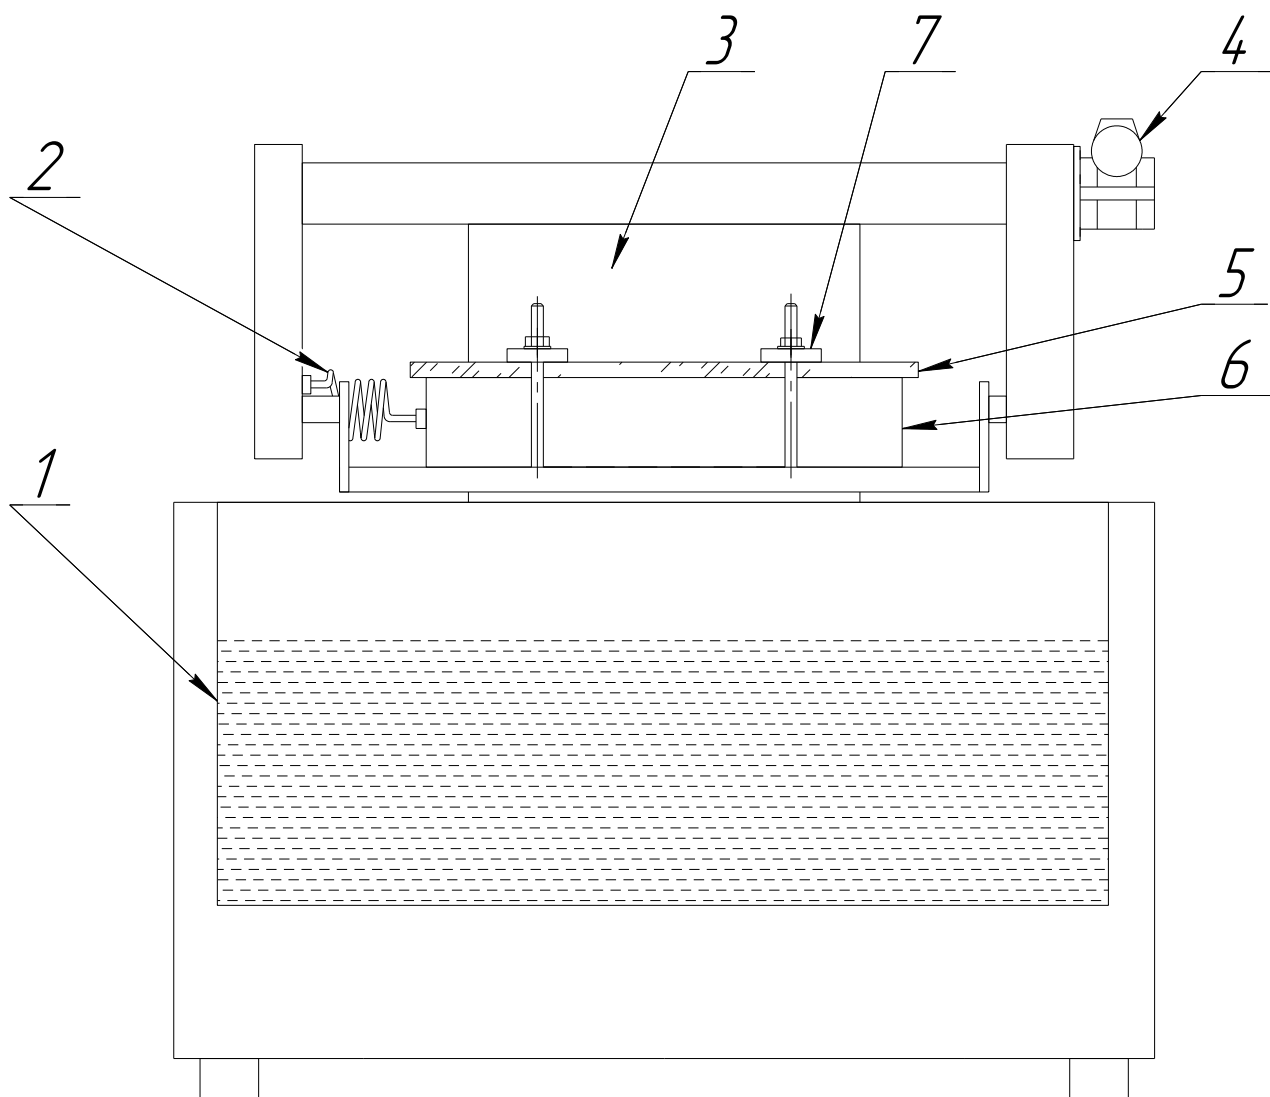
Общий вид станда для опрессовки ГБЦ.
